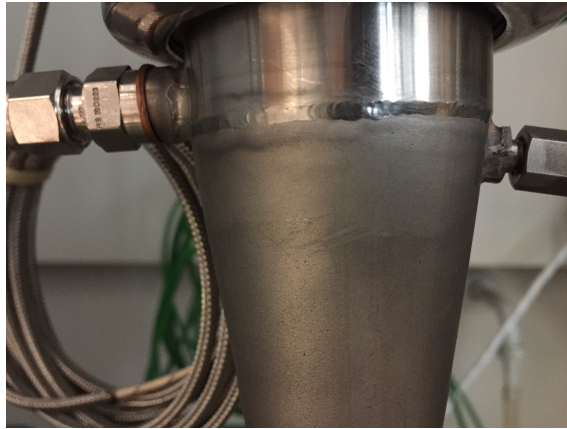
Soldadura entre la reducción 51/25 y la conexión NW50 Clamp.
